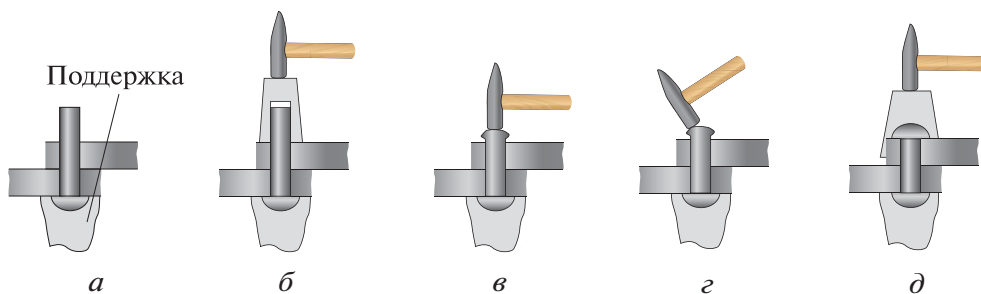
Соединение деталей заклёпками с полукруглой головкой:
